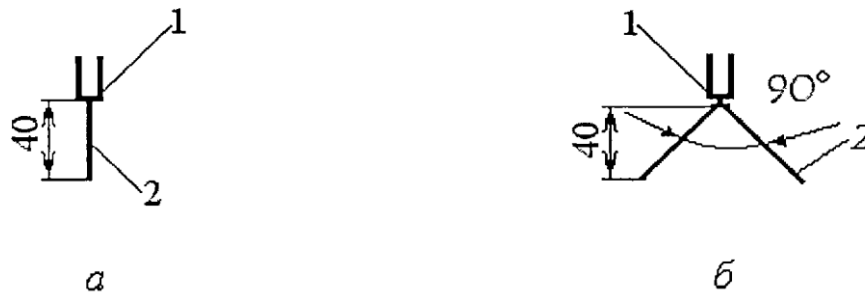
Форма зуба: а - прямой зуб; б - V - подобный зуб;
